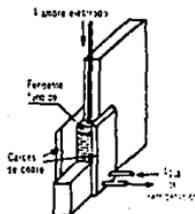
Esquema de soldadura con arco sumergido.
